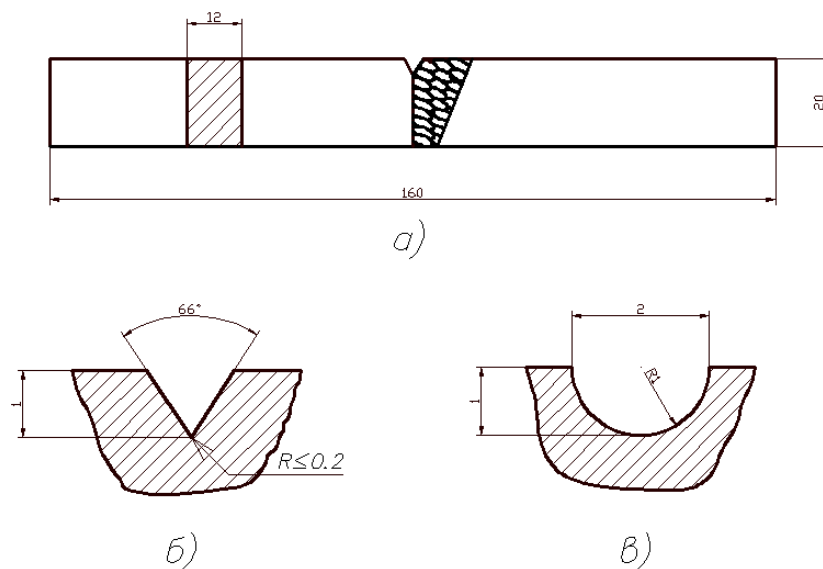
Плоский сварной образец (а) с краевым надрезом типа Шарпи (б) или Менаже (в)
